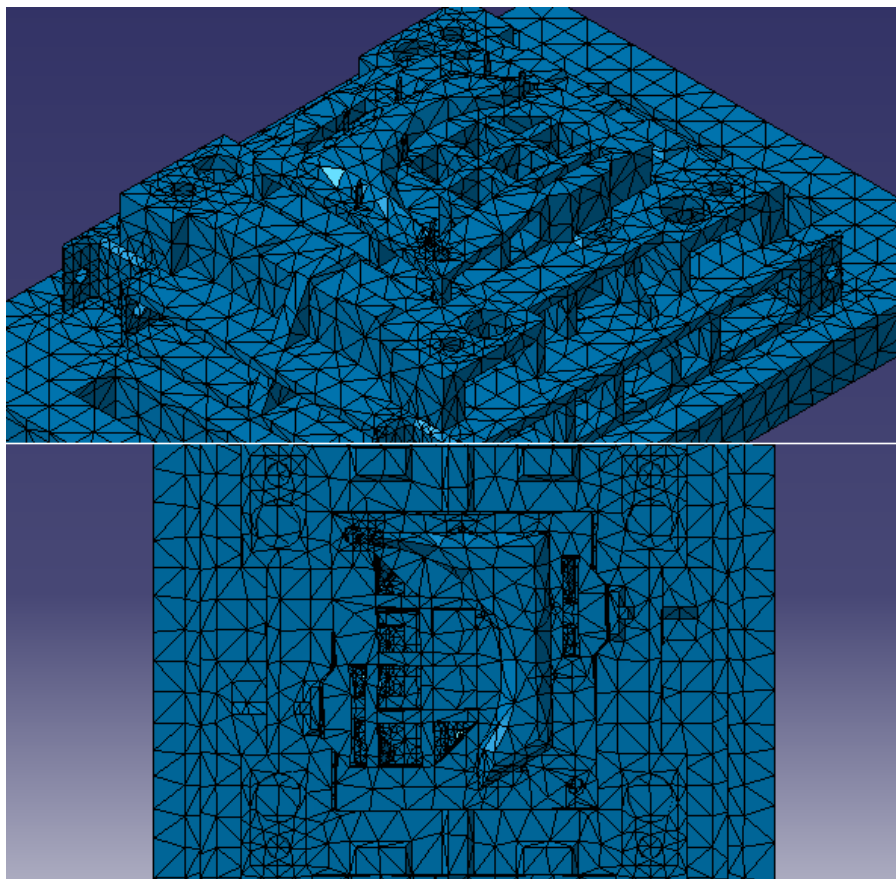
Deformada para espessura de 10mm (Fonte – Construção própria)
